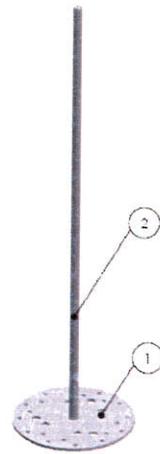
Anschlageinrichtung, Typ: ZSM 300-800 III B / B-S / HD-B / H
